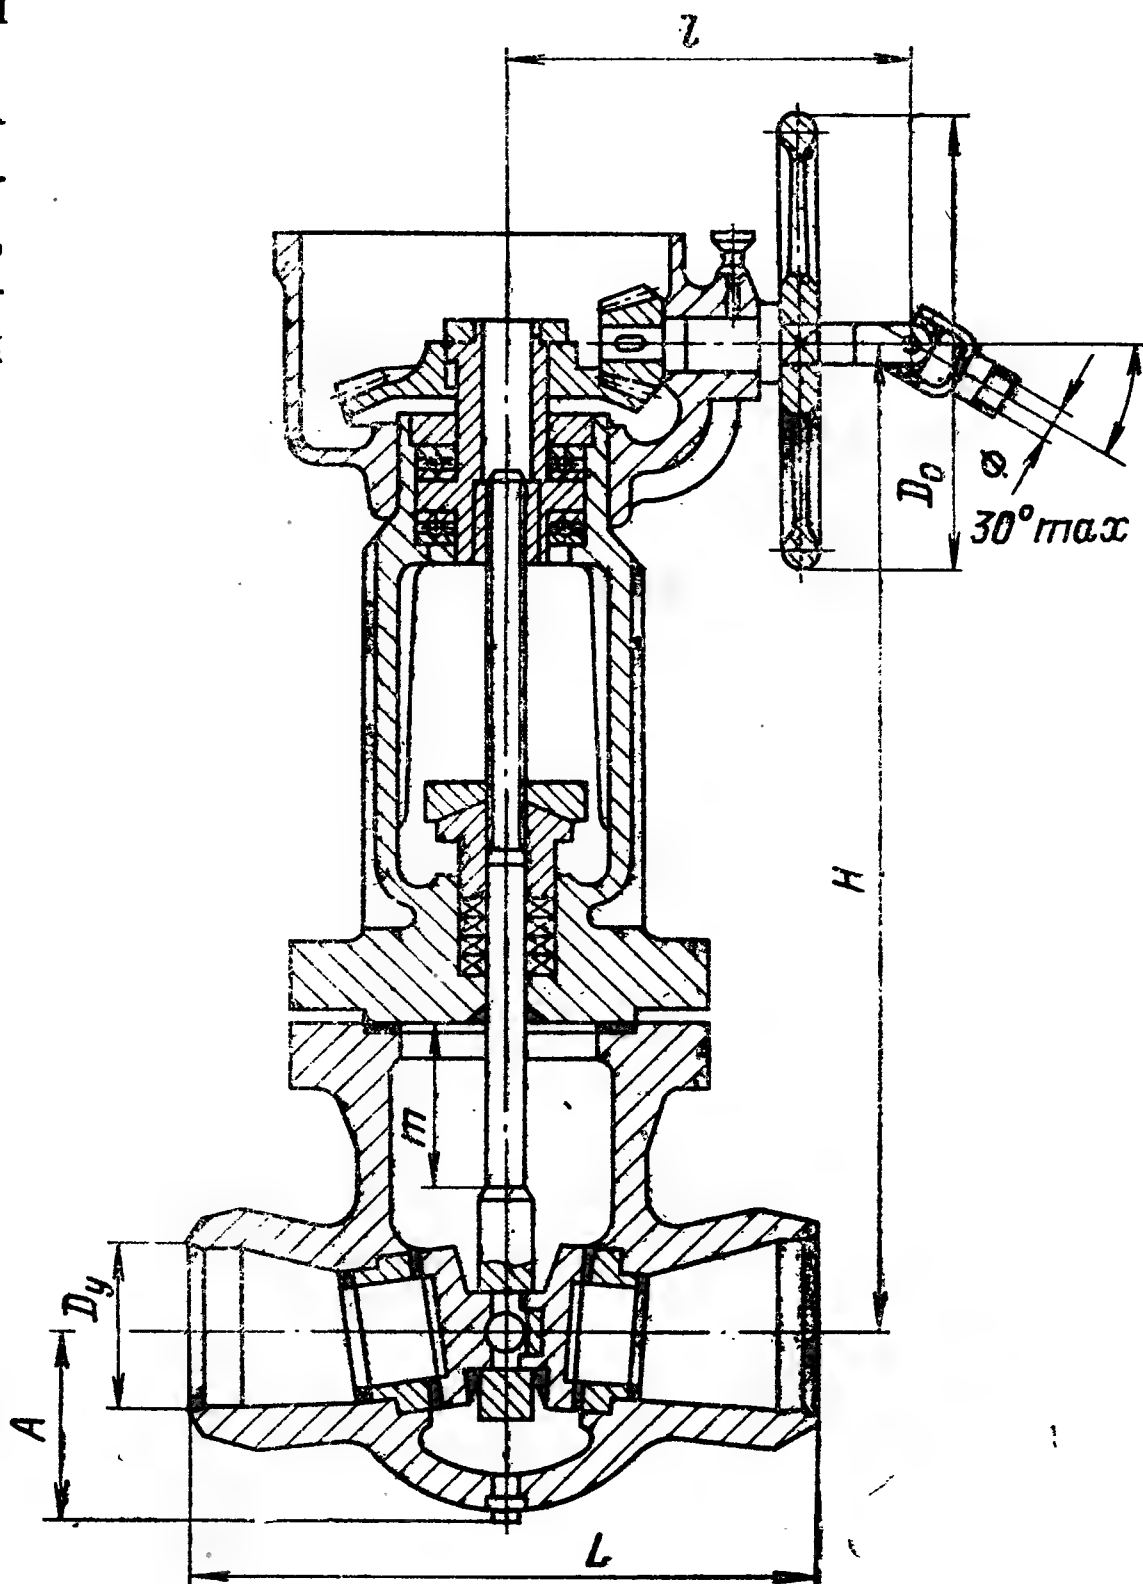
Задвижка стальная без фланцев, соединяемая с трубопроводом на сварке.
